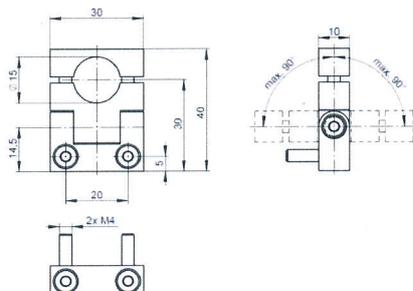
Support B2-LD-K, plan coté (mesures en mm)
